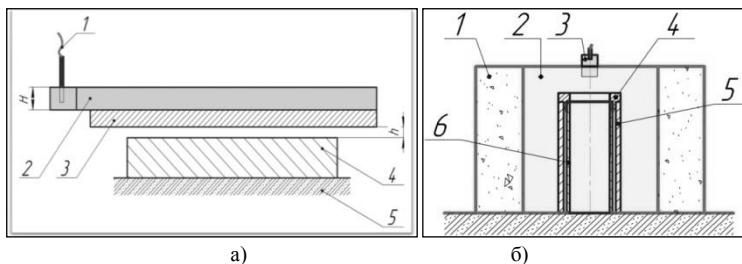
Технологические схемы сварки исходных материалов - а) схема сварки при параллельном расположении пластин: 1 – детонатор, 2- заряд взрывчатого вещества, 3 – метаемая пластина (Н65В2МЦ или ЭК102), 4- основа (ОХНЗМ), 5- базовая поверхность, h – сварочный зазор, H – высота заряда взрывчатого вещества; б) схема внутреннего плакирования трубы: 1 – забойка; 2 - взрывчатое вещество; 3 – детонатор; 4 – верхняя крышка; 5 – внешний слой (сталь ОХНЗМ); 6 – внутренний слой (ЭК102 и Н65В2МЦ)
